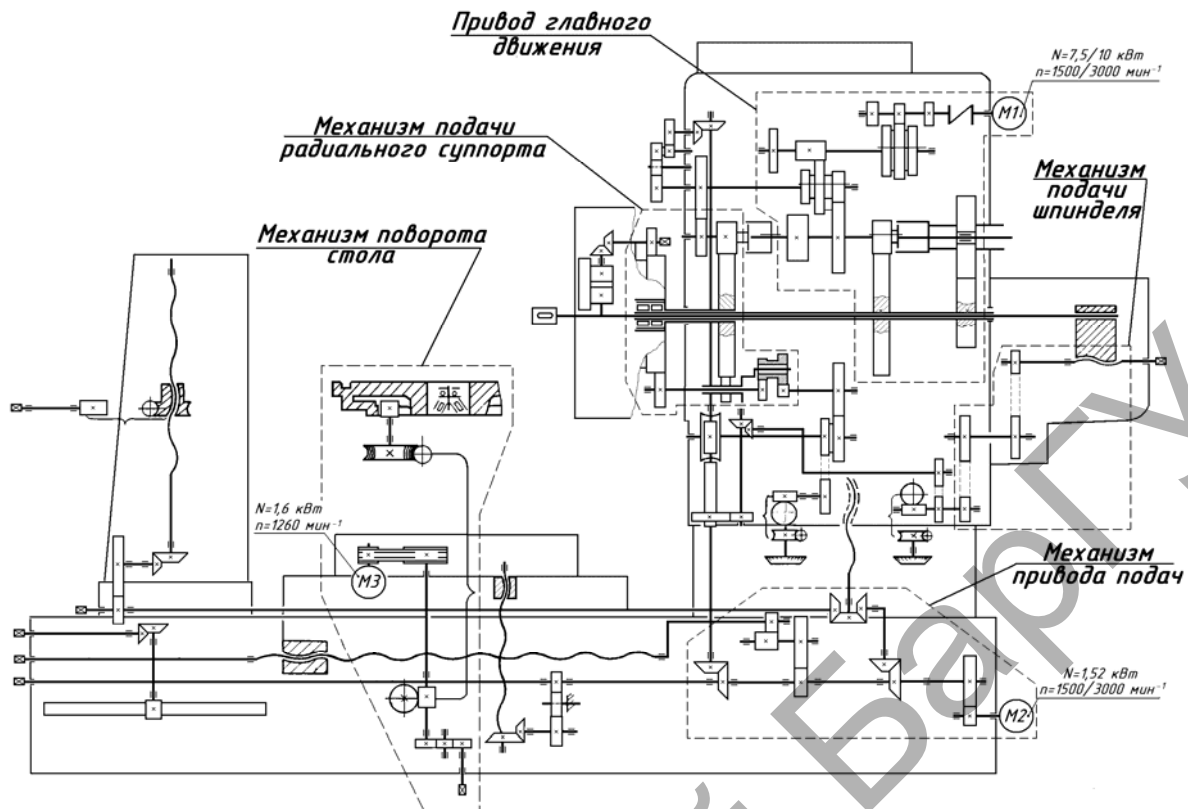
Кинематическая схема станка модели 2620В
